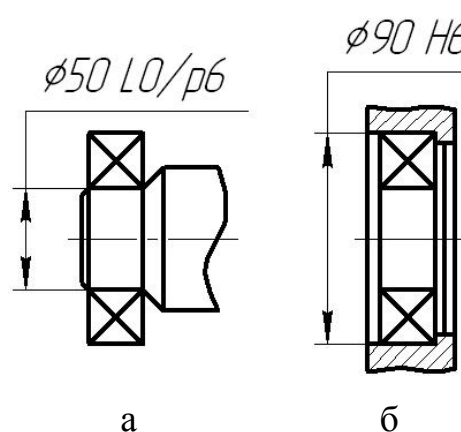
Обозначения посадок с кольцами подшипников качения: а – посадка внутреннего кольца на вал, б – посадка наружного кольца в корпус
